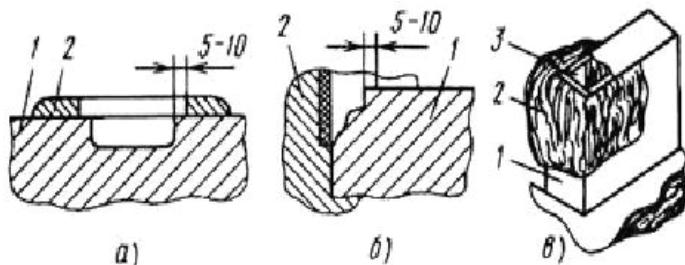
Формовка места сварки для горячей сварки чугуна:
